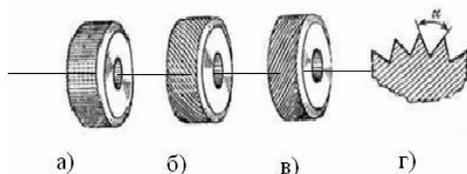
Ролики для накатки поверхностей: *a* – для прямой накатки; *б* – с левой насечкой; *в* – с правой насечкой; *г* – угол насечки
